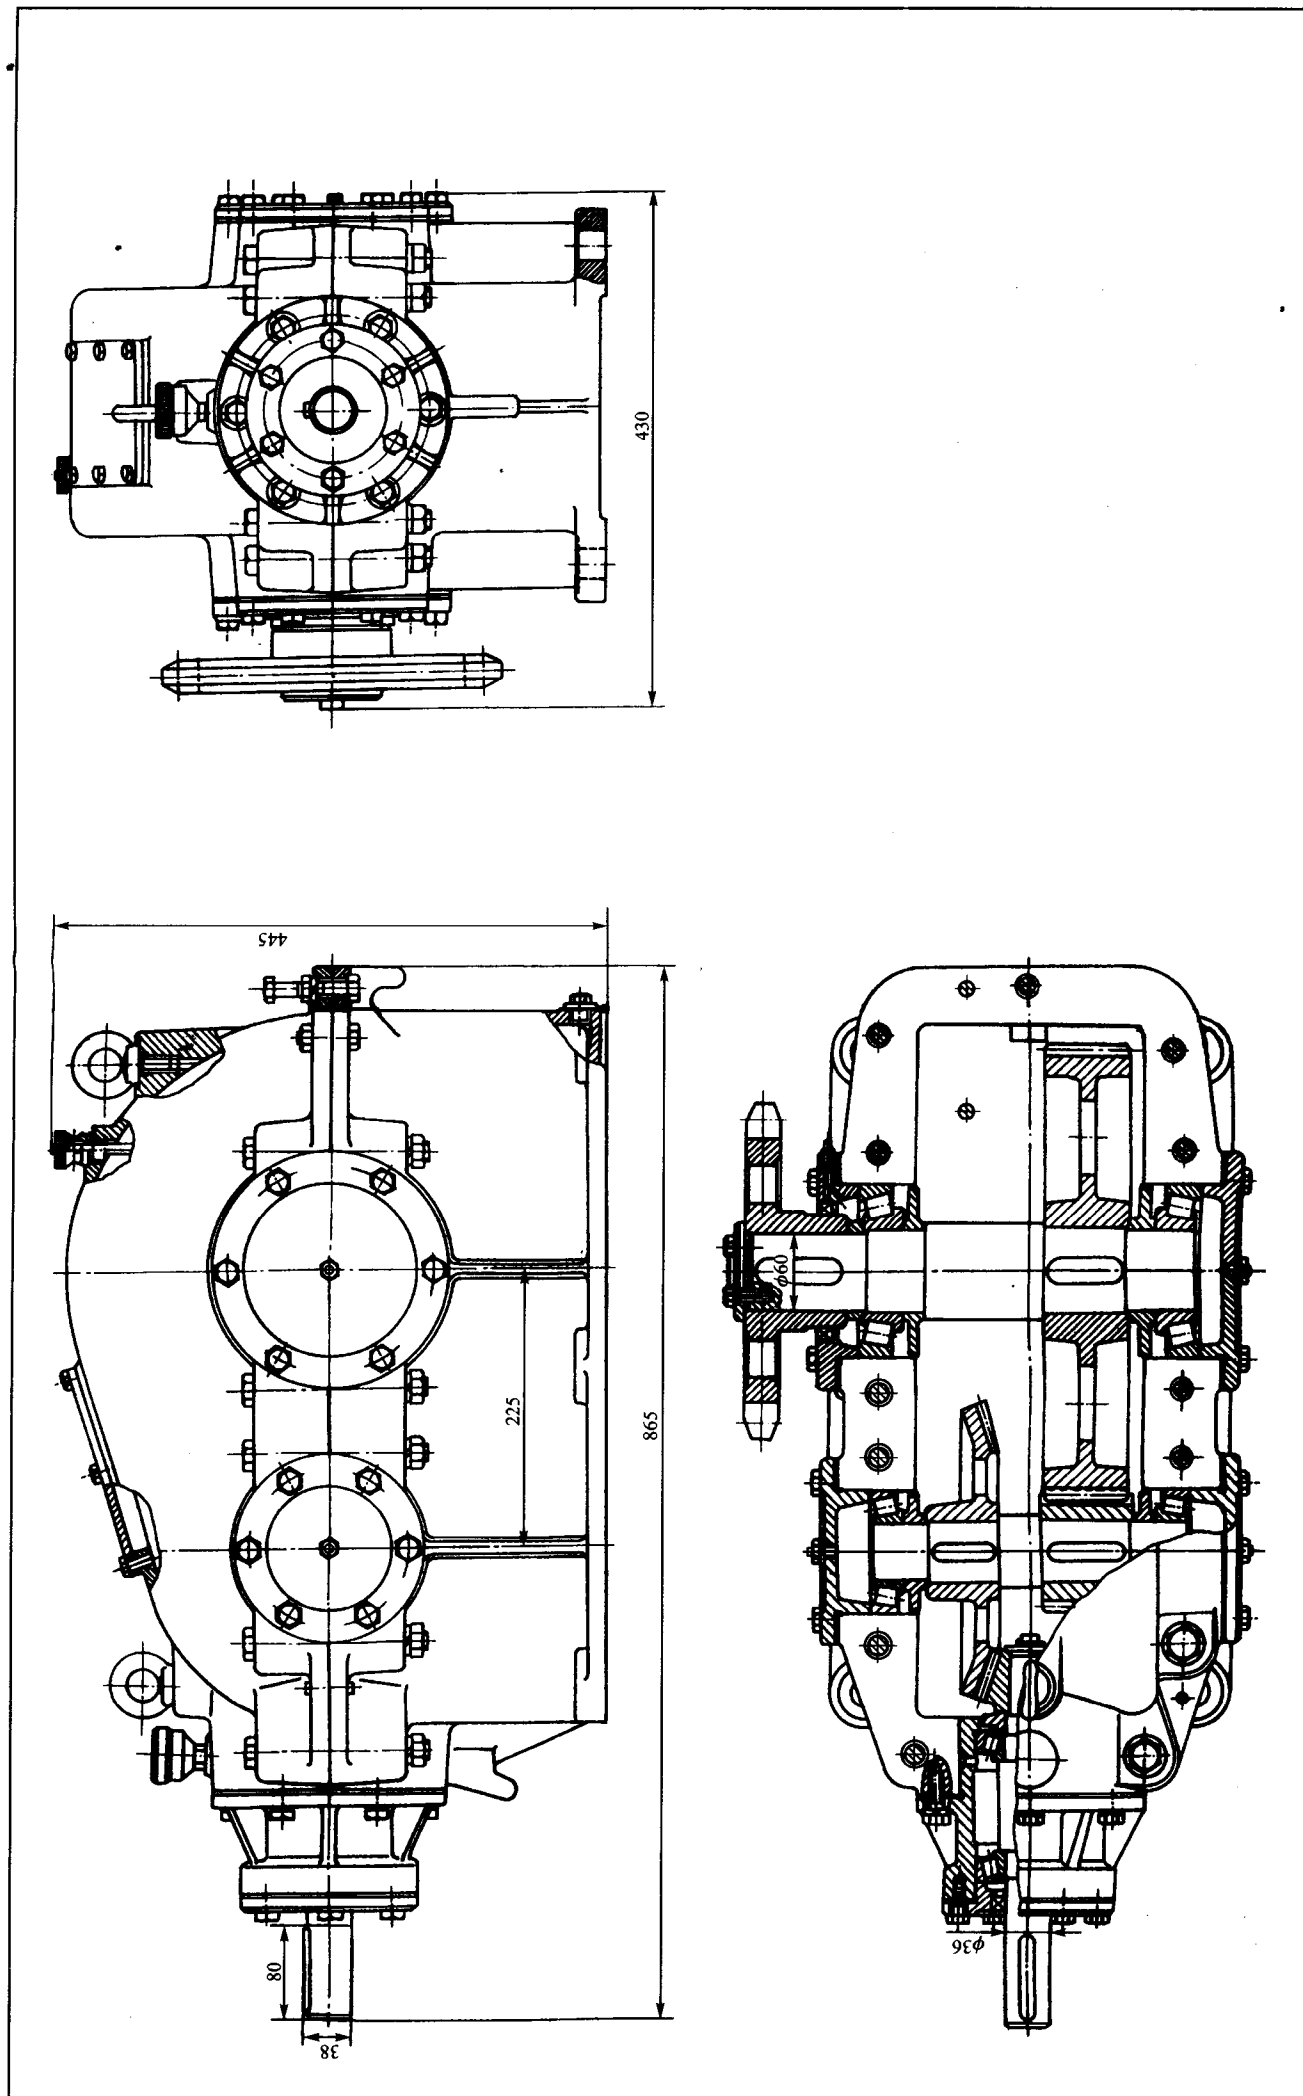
圆锥-圆柱齿轮减速器装配工作图 (一)
